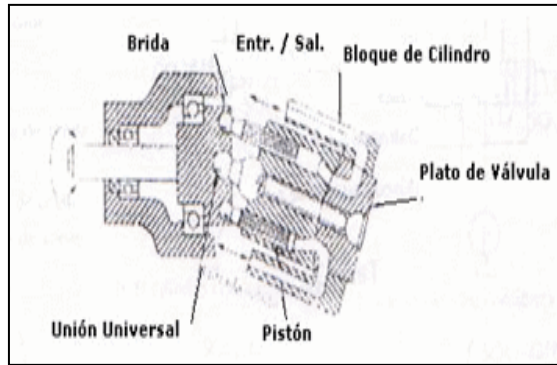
Motor hidráulico pistón eje inclinado [7].
